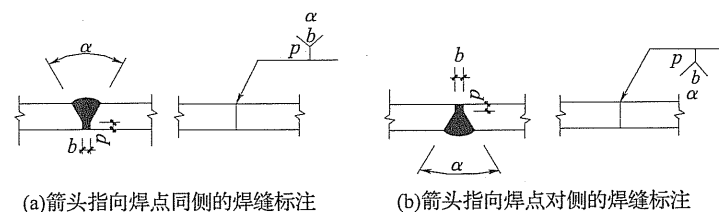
焊缝尺寸的标注原则
